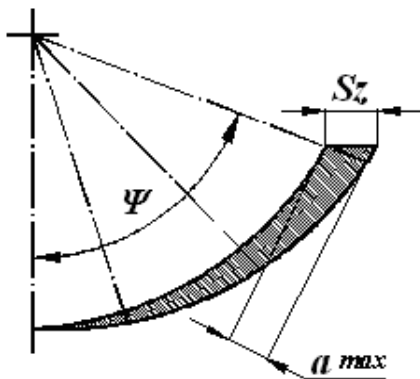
Схема утворення стружки при циліндричному фрезеруванні.
